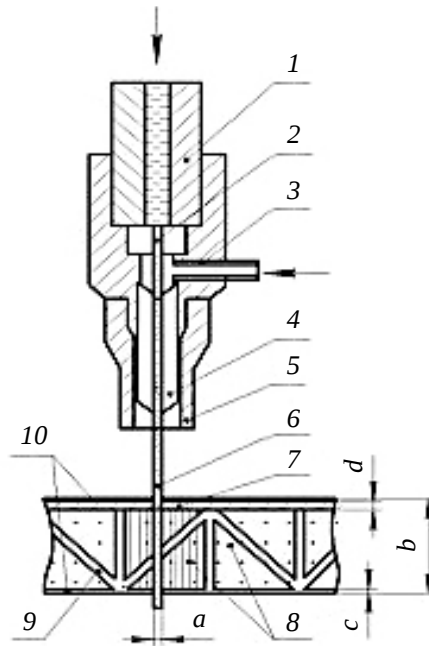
Схема гидроабразивного станка: a – толщина реза; b – толщина изделия из ПКМ; c – толщина обшивки; d – толщина металлической вставки; 1 – магистраль для подвода воды под высоким давлением; 2 – сопло; 3 – патрубок для подачи абразива; 4 – смеситель; 5 – кожух; 6 – режущая струя воды с абразивом; 7 – металлическая вставка в панели из ПКМ; 8 – внутренняя структура панели из разнородных наполнителей; 9 – внутреннее ребро жесткости панели; 10 – верхняя и нижняя обшивки панели [21]
